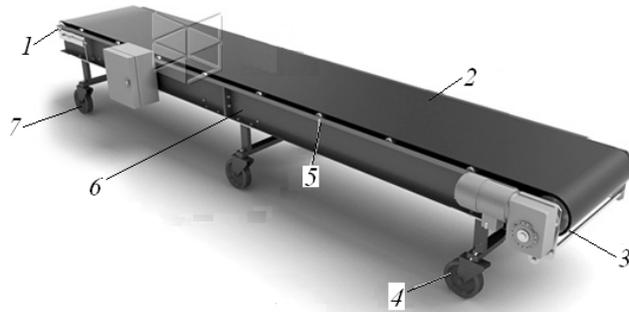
Базова конструкція стрічкового конвеєра:
